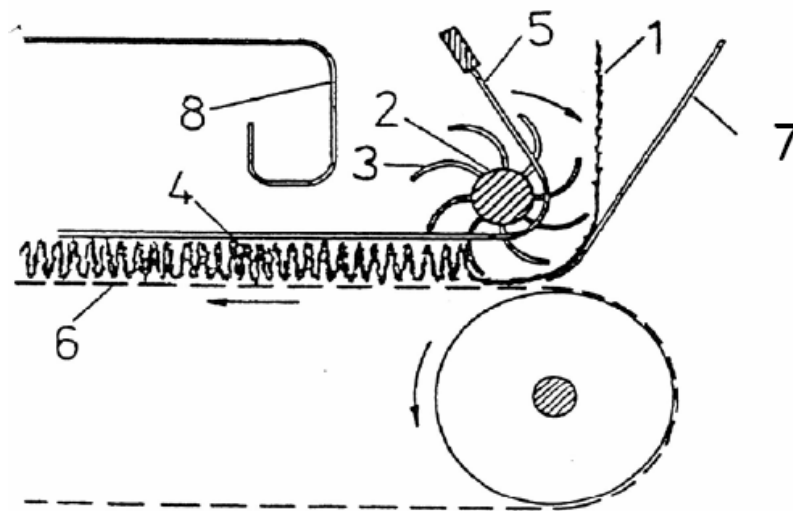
Vibračný kolmý ukladač pavučiny [10]
